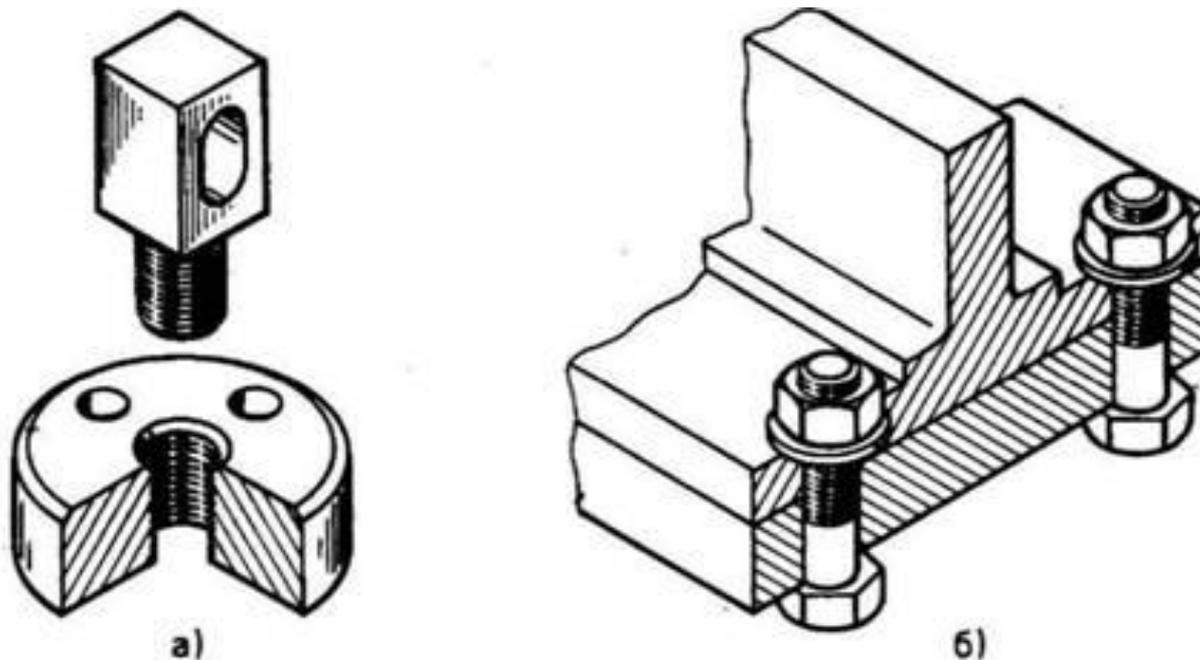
Основные виды резьбовых соединений: а — непосредственным свинчиванием; б - с помощью болта
